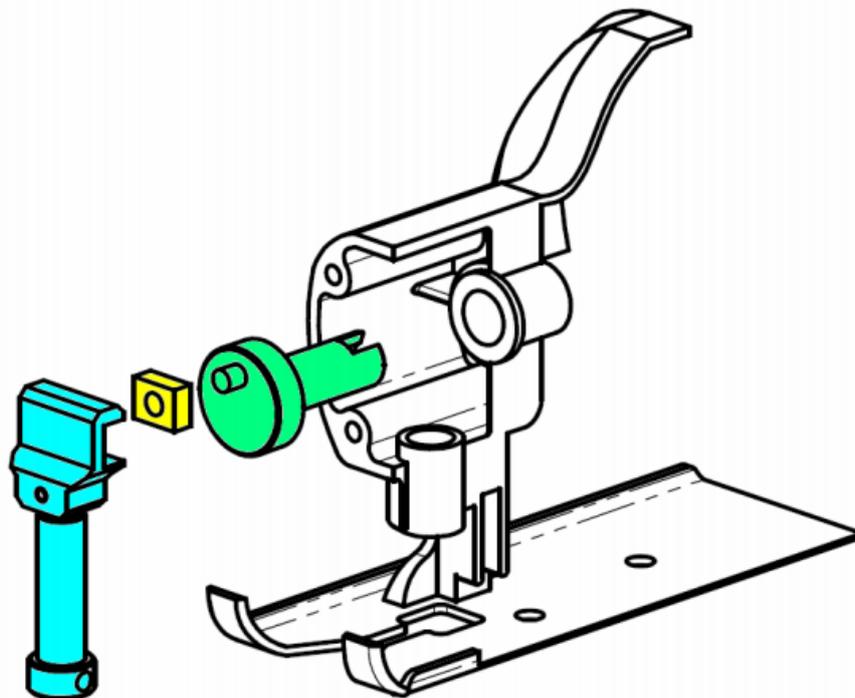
Vue en éclaté de la scie-sauteuse.
